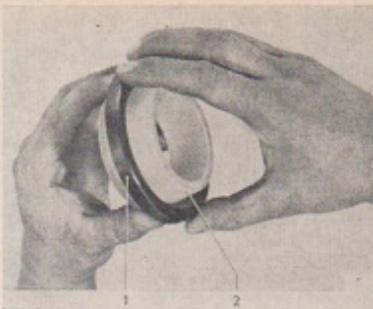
Wellendichtring für hinteres Hauptlager auf Schutzhülse von S-1296 aufziehen
